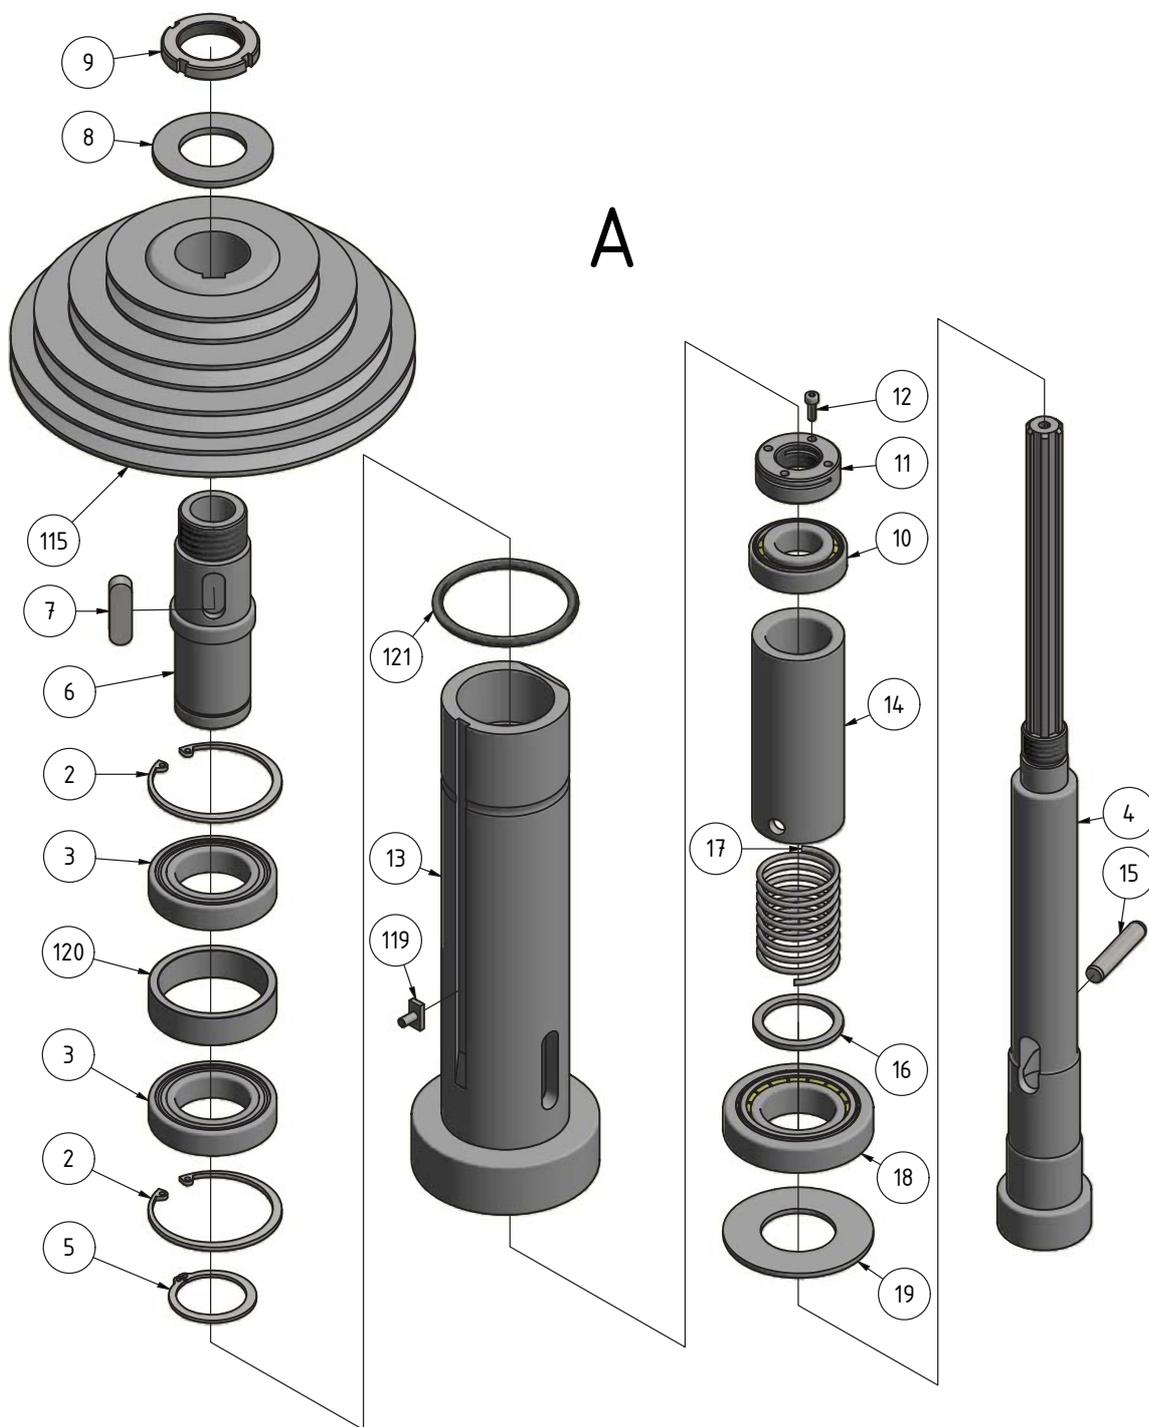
Bohrkopf 1 von 5 - Drilling head 1 of 5
